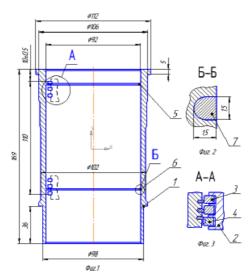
Гильза цилиндров с двумя кольцевыми пазами
